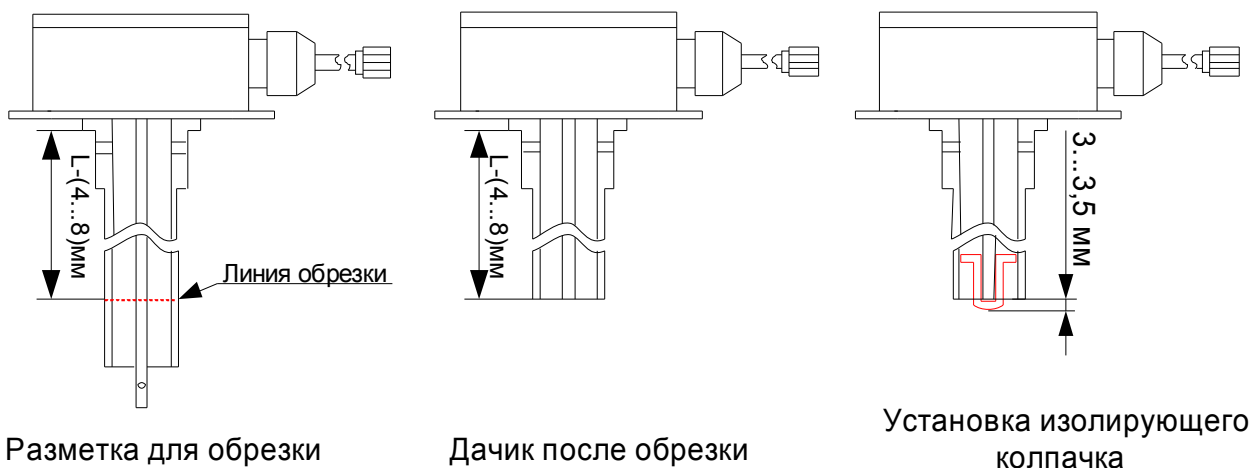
Разметка для обрезки, обрезка датчика до требуемой длины и установка изолирующего колпачка.
